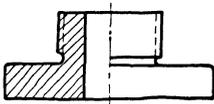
Bolzenschraube, halb Schnitt, halb Ansicht.
